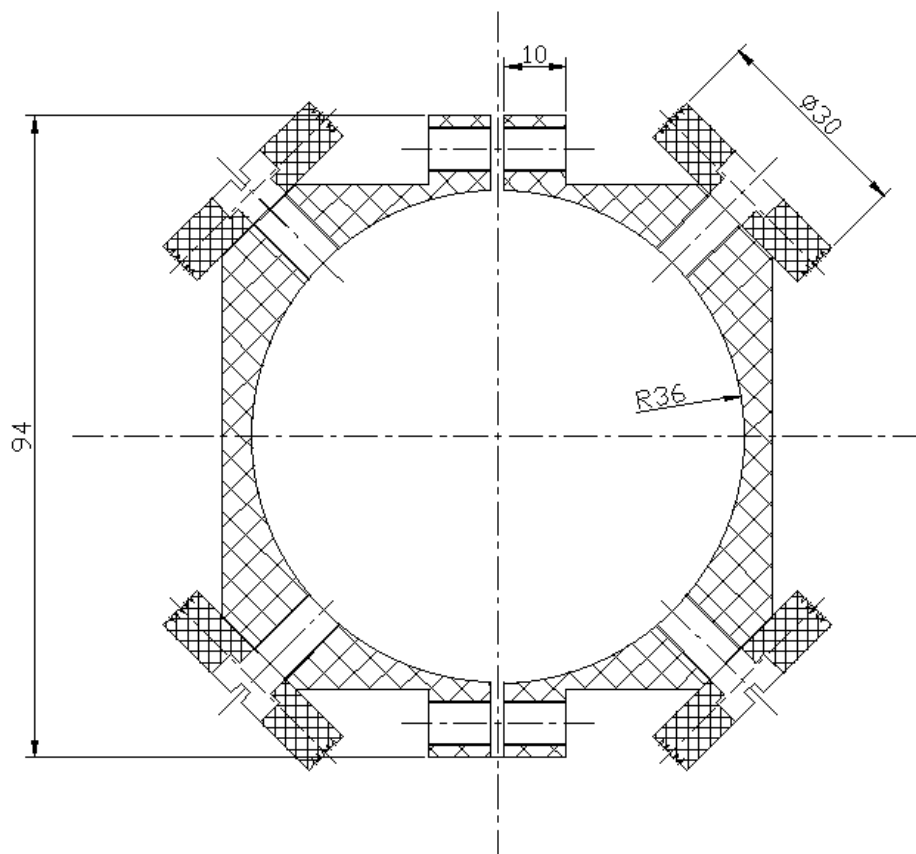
Сборочный чертеж держателя и датчиков магнитного поля
